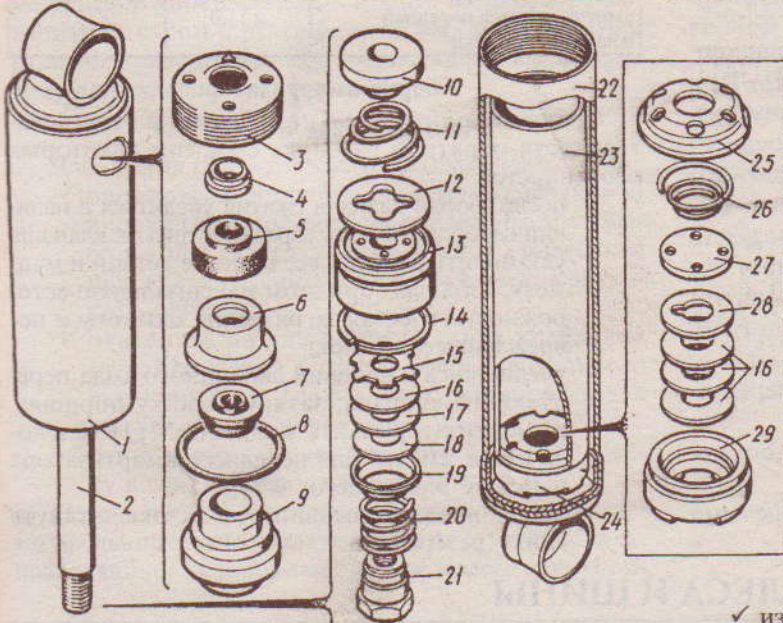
Детали амортизатора передней подвески: 1 - кожух амортизатора; 2 - шток амортизатора с проушиной в сборе; 3 - гайка резервуара амортизатора; 4 - кольцо защитное; 5 - прокладка; 6 - обойма манжеты штока амортизатора; 7 - манжета; 8 - кольцо уплотнительное резервуара амортизатора; 9 - втулка направляющая штока амортизатора; 10 - тарелка ограничительная перепускного клапана; 11 - пружина; 12 - тарелка; 13 - поршень амортизатора; 14 - кольцо; 15 - диск дроссельный клапана отдачи; 16 - диск толщиной 0,4 мм; 17 - диск толщиной 0,2 мм; 18 - шайба; 19 - тарелка упорная; 20 - пружина; 21 - гайка; 22 - резервуар амортизатора в сборе; 23 - цилиндр; 24 - клапан сжатия амортизатора в сборе; 25 - обойма клапана сжатия амортизатора; 26 - пружина впускного клапана амортизатора; 27 - тарелка клапана сжатия амортизатора; 28 - диск дроссельный клапана сжатия амортизатора; 29 - корпус клапана сжатия амортизатора
